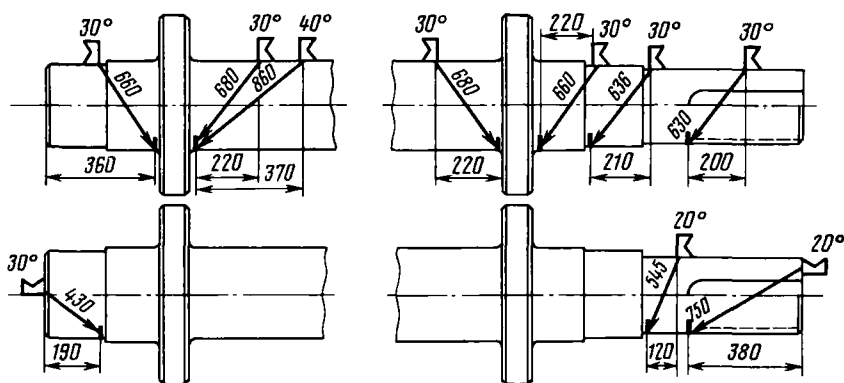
Схема и зоны контроля наклонными искателями главного приводного вала эскалатора ЭМ-4
